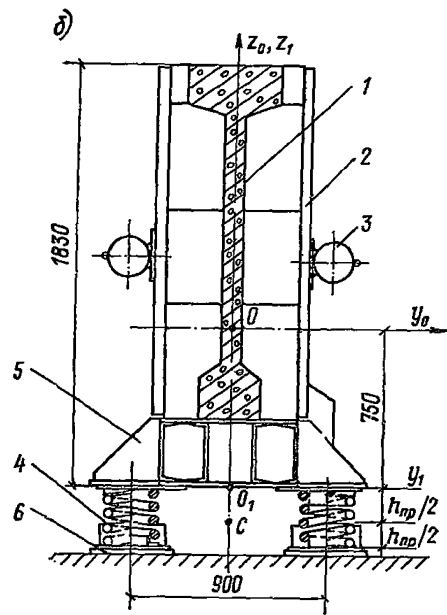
Виброизолированная стендовая силовая виброформа 74 для изготовления железобетонных стропильных балок 1В4-18-3 (а). Разрез А—А (б)
